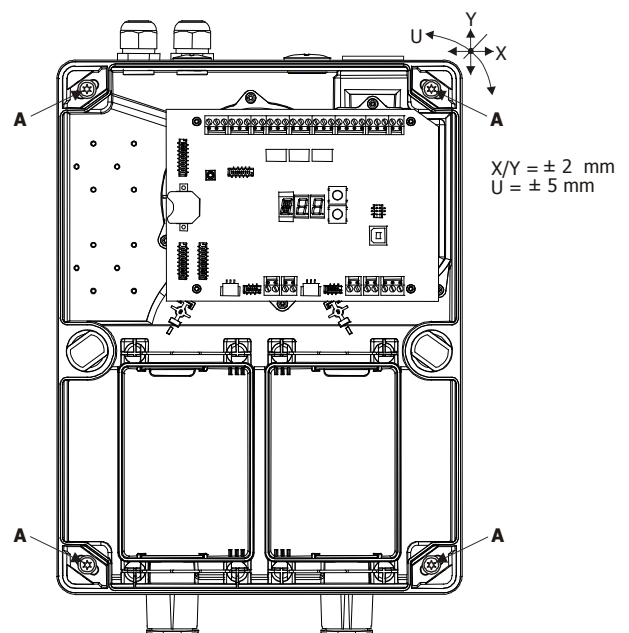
Apertura, chiusura e fissaggio dello DFA05
